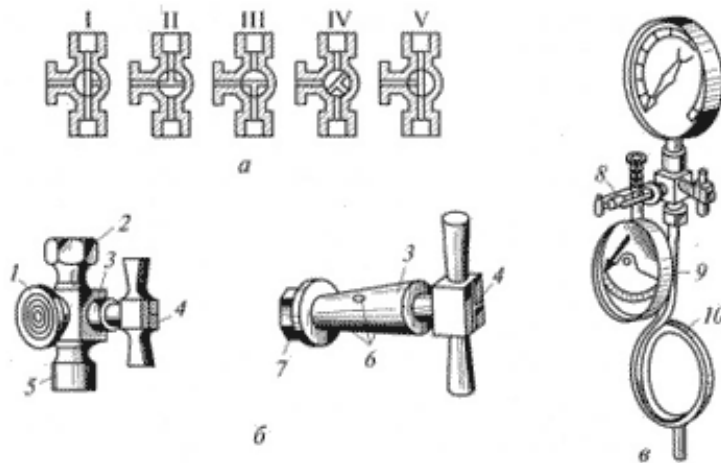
Трехходовой кран: а-положения I—V трехходового крана; б-детали крана; в-крепление контрольного манометра для проверки рабочего манометра; I-рабочее положение; II-постановка стрелки на ноль; III-продувка сифонной трубки; IV-промежуточное положение (набор конденсата в сифонной трубке); V-проверка рабочего манометра контрольным; 1-фланец для контрольного манометра; 2-штуцер для манометра; 3-пробка крана; 4-риски; 5-ниппель для сифонной трубки; 6-отверстия в пробке; 7-гайка для затяжки пробки; 8-скоба; 9-контрольный манометр; 10-сифонная трубка.
